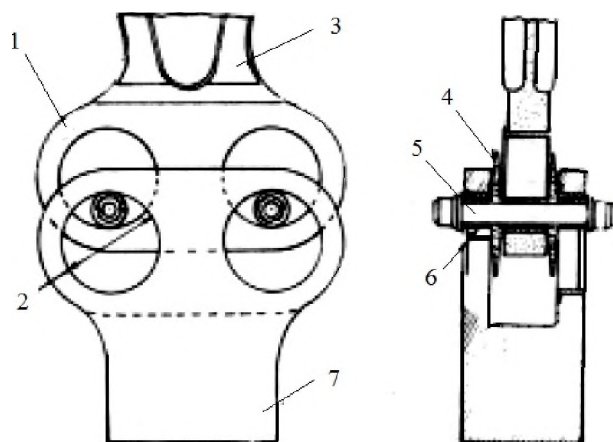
Схема и компоновка бифилярного маятникового гасителя колебаний [26]:
